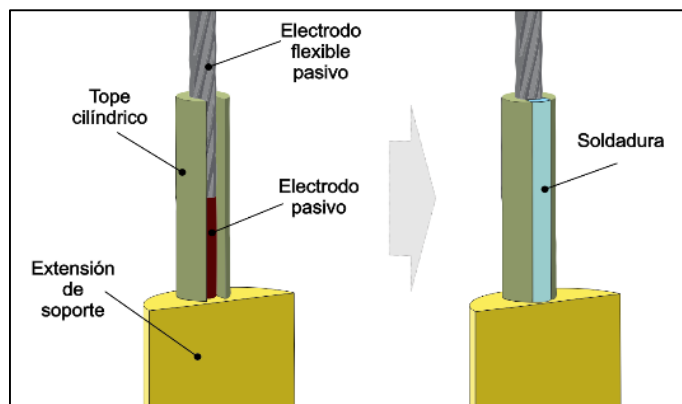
Esquema de la disposición de los elementos a soldar y la soldadura terminada
